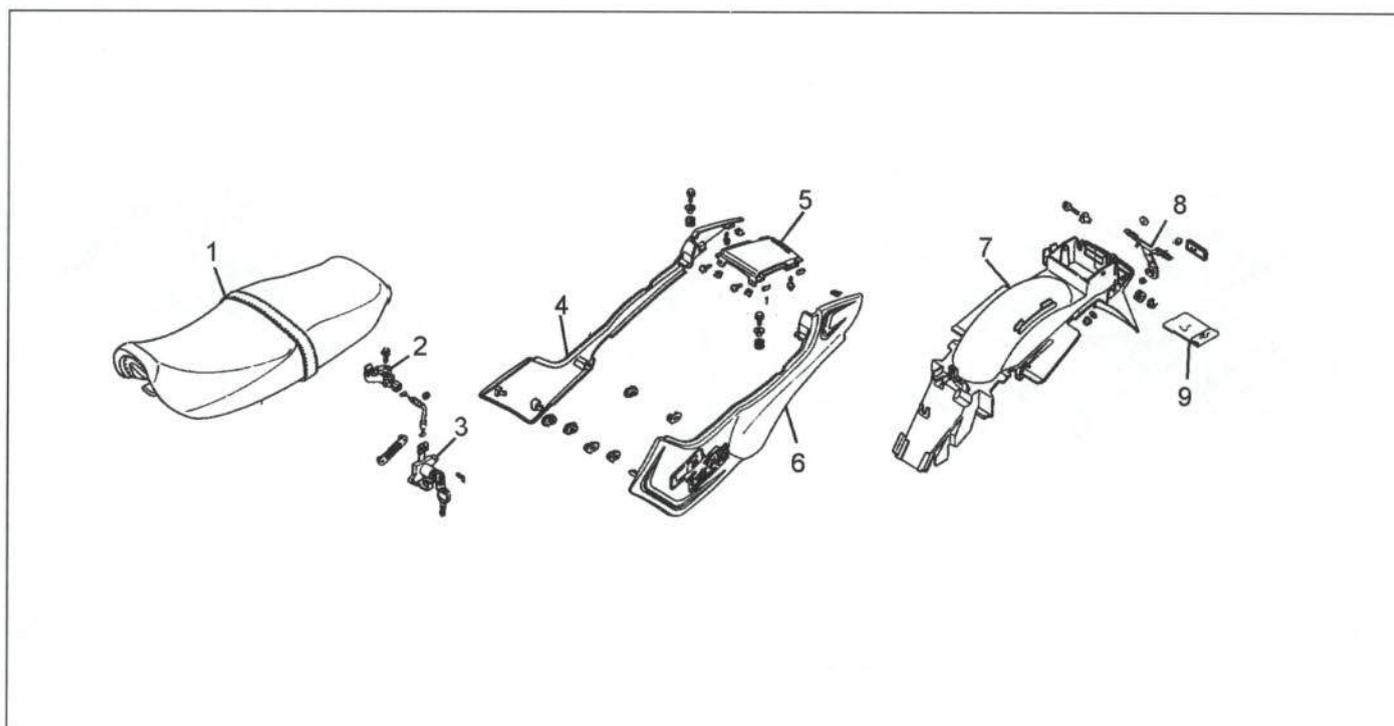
Despiece de las piezas exteriores de la parte trasera
